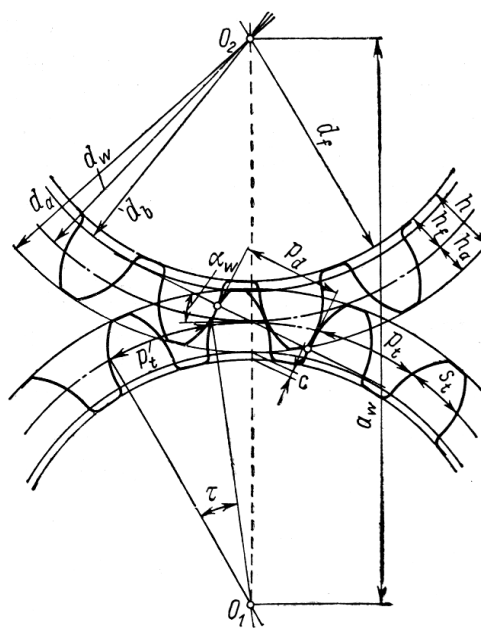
Элементы цилиндрических зубчатых колес и передач
